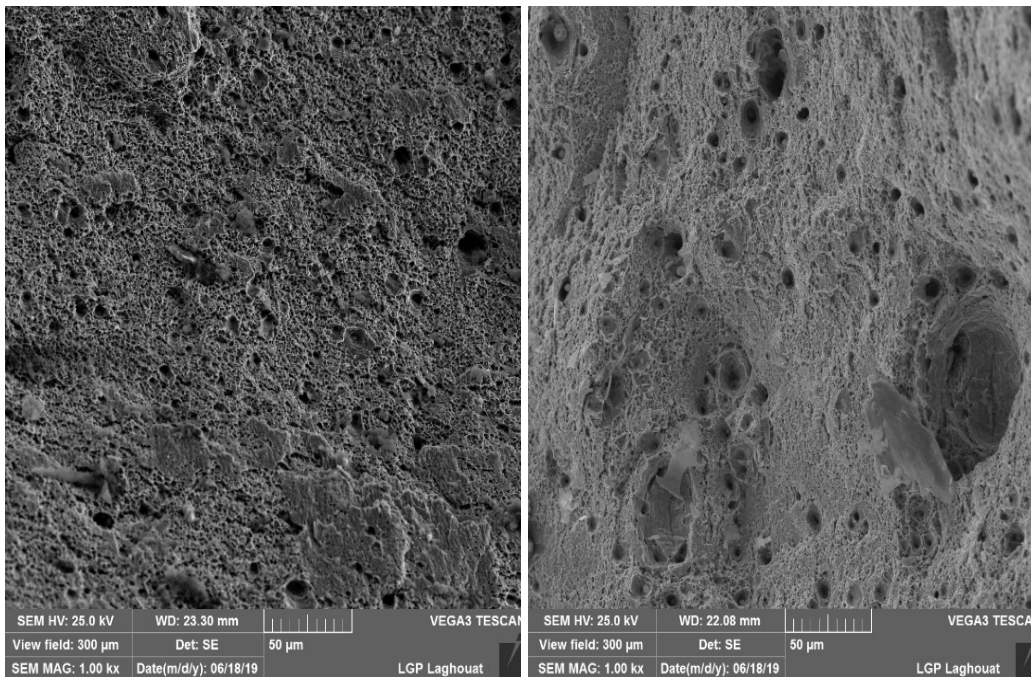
Fractographies des éprouvettes soudée et revenu à 650 °C, a) avant et b) après le traitement de vieillissement
